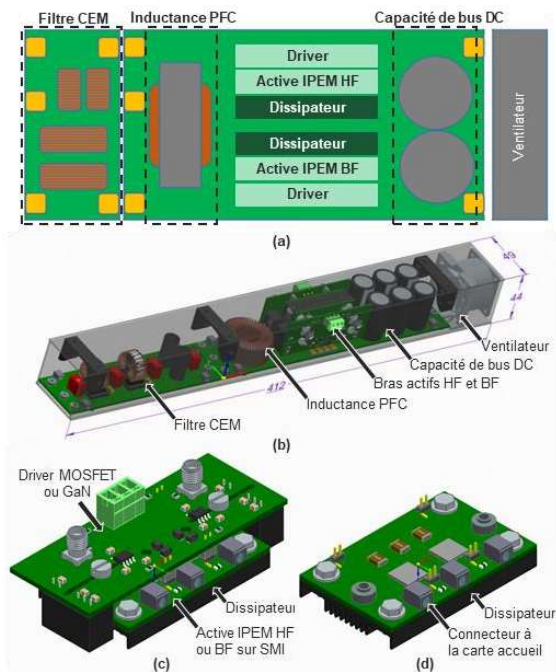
Représentation schématique du prototype (a), vue de l'assemblage 3D sur SolidEdge (b), vue de l'ensemble d'un des deux Active IPEM sur SolidEdge (c), vue du BF Active IPEM sur SolidEdge (d)
